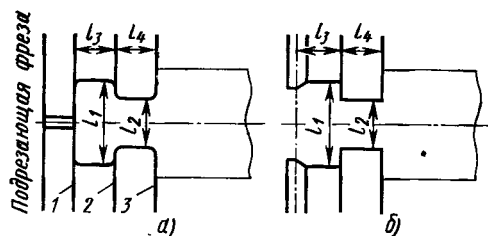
Профили комплектов фрез для Т-образных хвостов:
